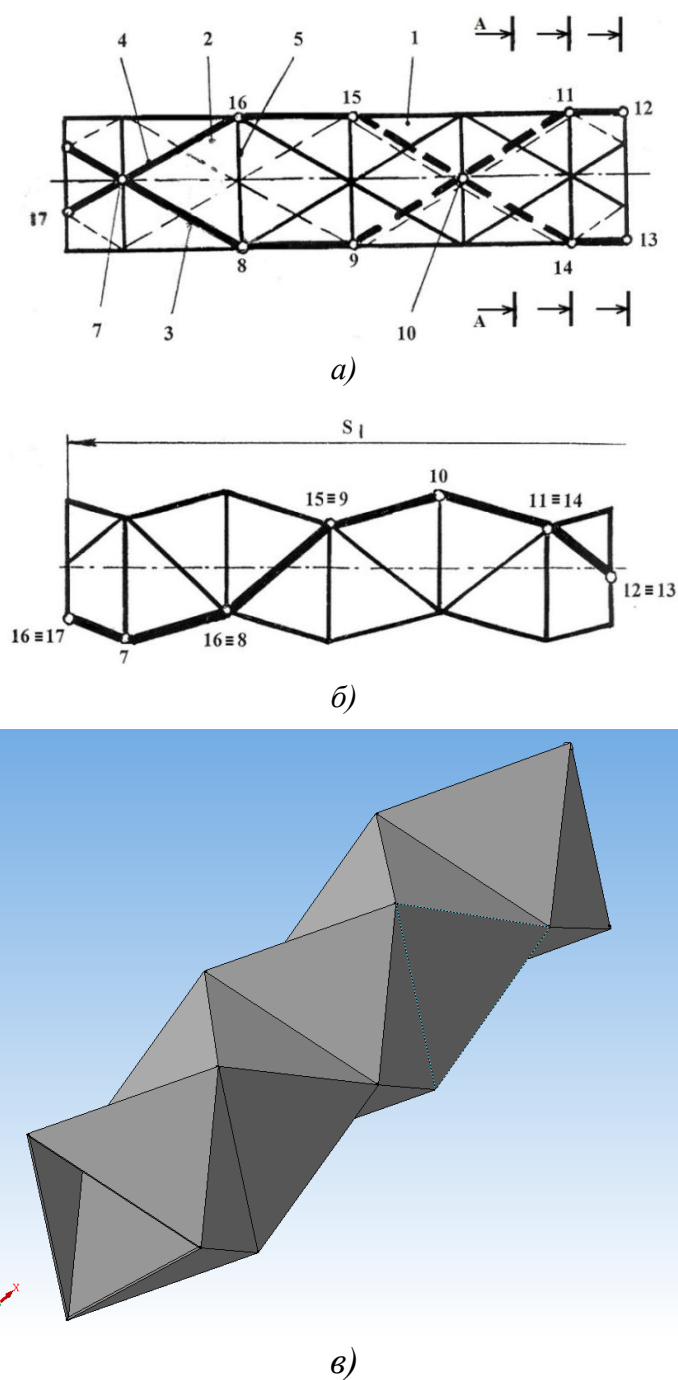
Рабочий орган станка для отделочно-зачистной и упрочняющей обработки обрабатываемых деталей (ОЗиУО), а) - вид спереди, б) - вид сверху, в) - наглядное изображение
